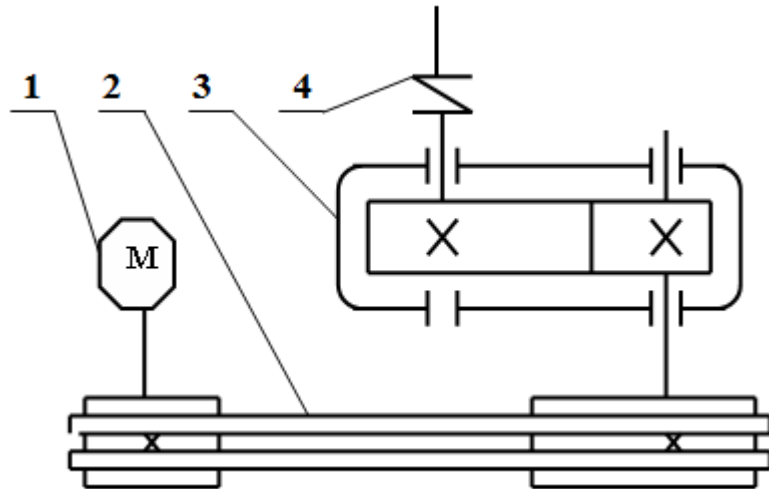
Привод коливного конвеєра: 1 – електричний двигун, 2 – пасова передача, 3 – одноступінчатий прямозубий циліндричний редуктор, 4 – муфта типу МПВП.
